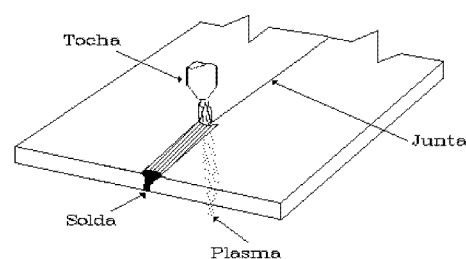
Modo “keyhole” de Soldagem por Plasma.
